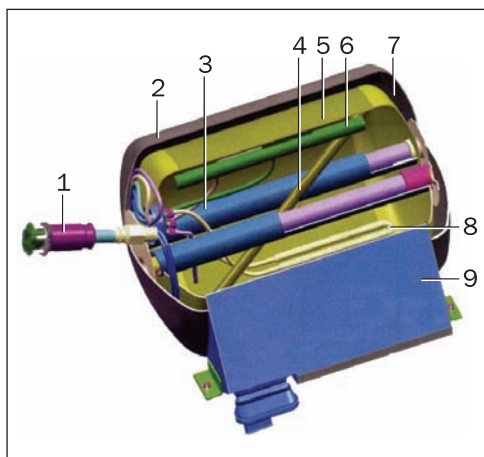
Компания BMW совместно с фирмой Magna Steyer разработала конструкцию «безопасного» топливного бака для сжиженного водорода: 1 — заправочное устройство; 2 — наружный бак; 3 — опоры; 4 — датчик уровня; 5 — внутренний бак; 6 — заправочная линия; 7 — изоляция и вакуум; 8 — нагреватель; 9 — крепежная коробка
